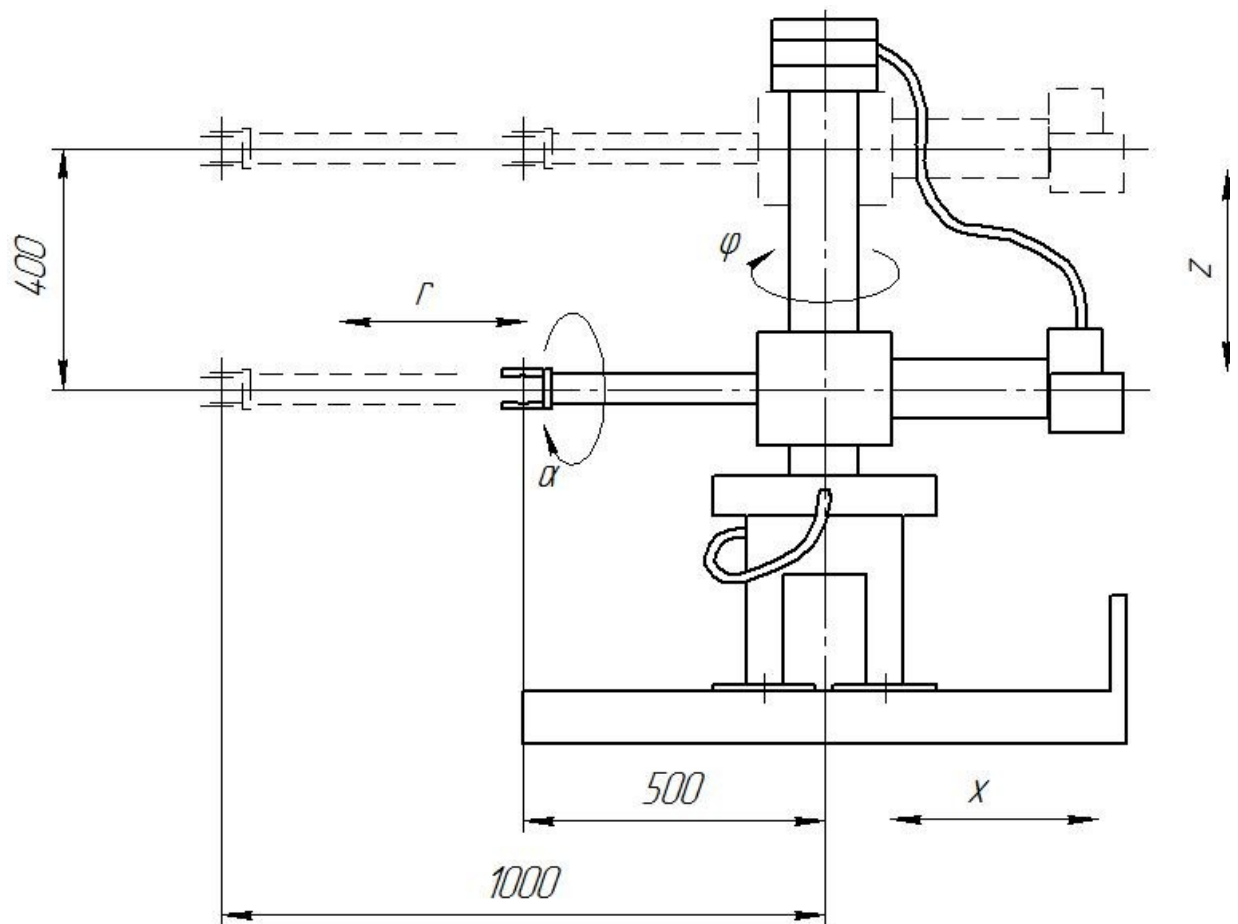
Эскиз робота и основные движения руки робота
